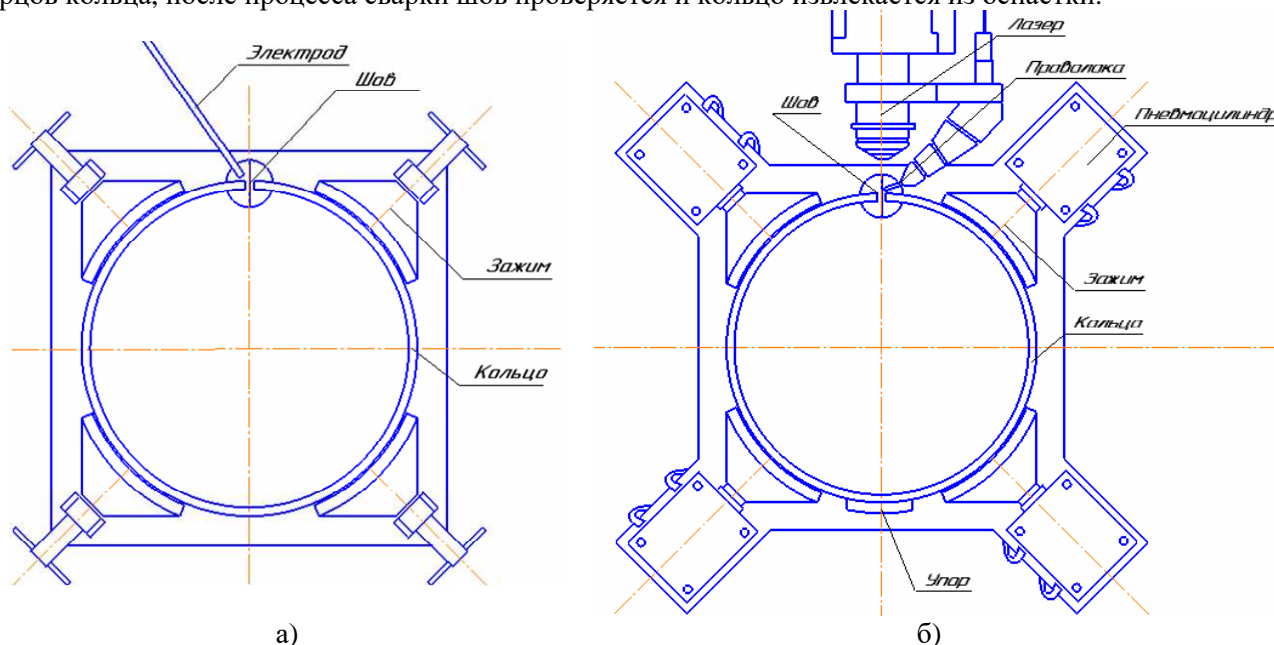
Кольцо, зафиксированное в оснастке для процесса: а) ручной и б) автоматической лазерной сварки
